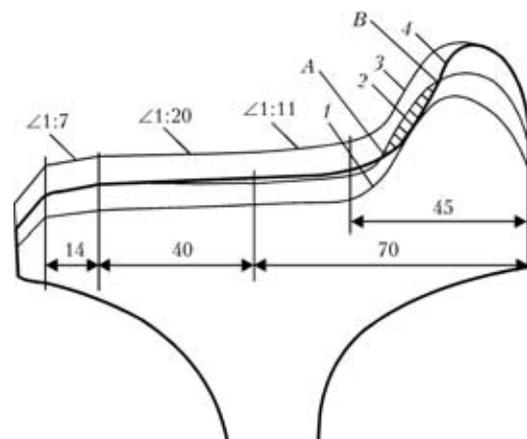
Схема восстановления профиля колеса: 1, 2 — линии обточки после наплавки гребня (А — начало; В — окончание наплавки); 3 — линия обточки после восстановления колес наплавкой гребня и обода; 4 — линия изношенной поверхности колеса
